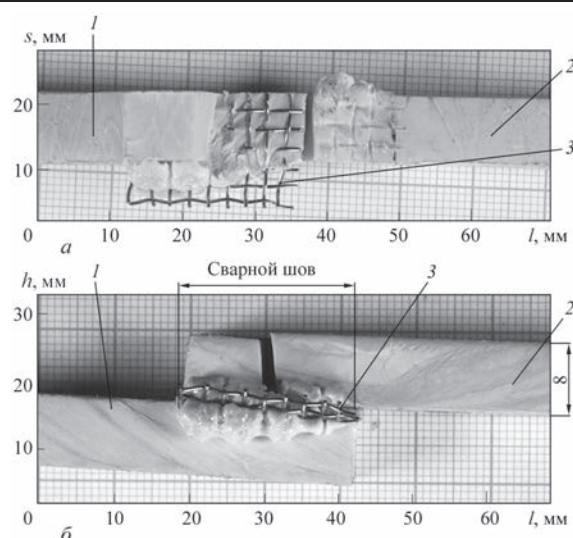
Характер разрушения образца (l — длина, h — высота, s — ширина), вырезанного из равнопрочного нахлесточного сварного соединения полимерного материала ZX-410: а — вид сверху; б — вид сбоку (1 — образец 2; 2 — образец 1; 3 — закладной элемент)
